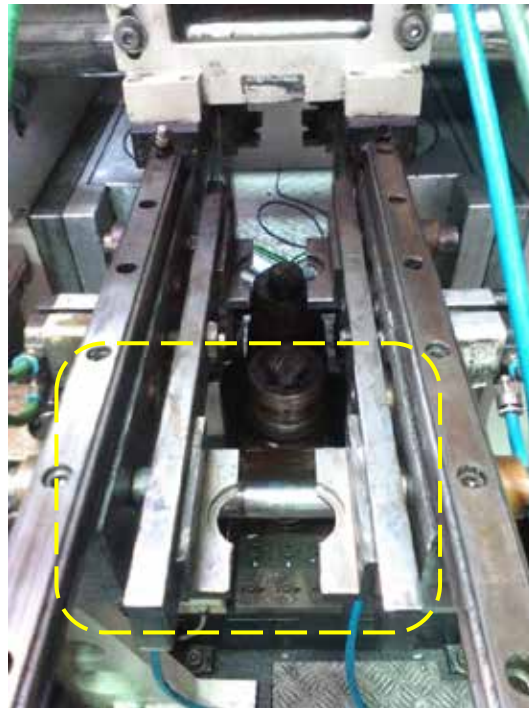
Cilindro neumático de la mesa del posicionador de la máquina
